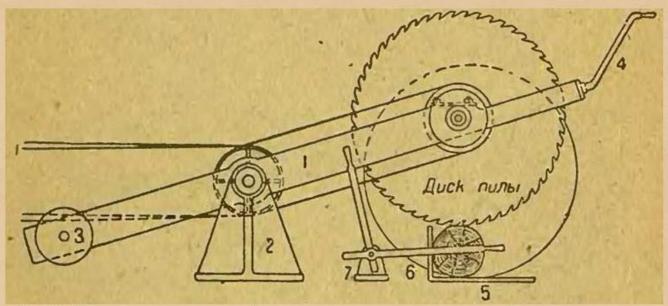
Круглая пила с противовесом, 1 — качающаяся рама, которую можно поднимать и опускать вместе с пилой, 2 — опорная плита, 3 — противовес. 4 — рычаг для поднимания и опускания пилы рукой, 5 — металлическая площадка, б — упор, 7 — стойка с откидными упорными шаблонами для регулирования
